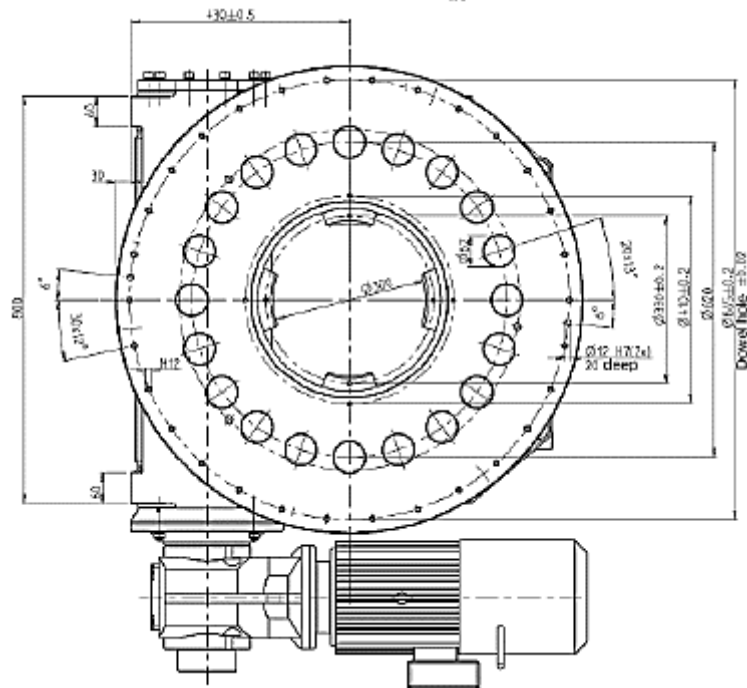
Vista en planta y de la consola de la Mesa giratoria EXPERT-TÜNKERS EDH1170/A7095
